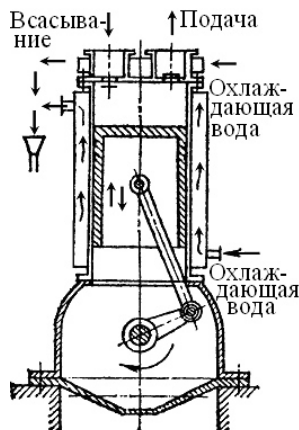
Конструктивная схема поршневого нагнетателя
